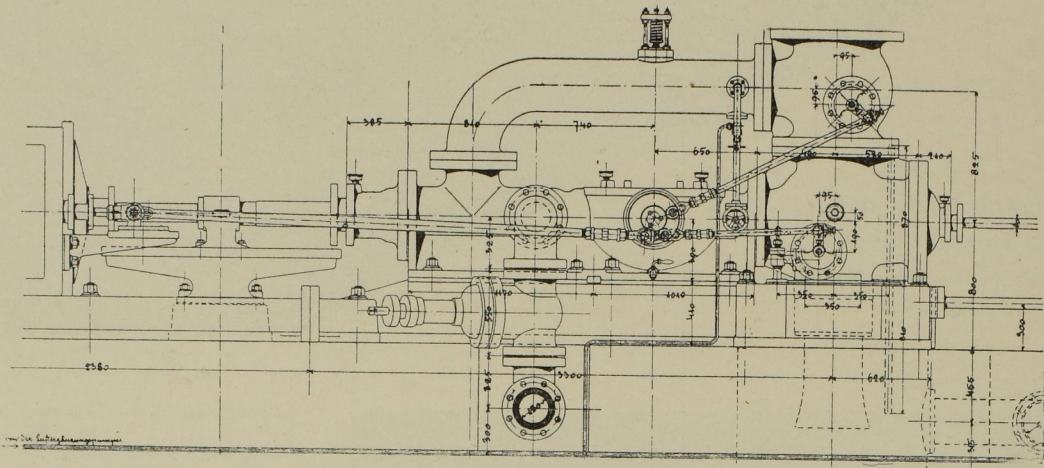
Seitenansicht der Pumpe mit Steuerung. Masst. 1:45.
